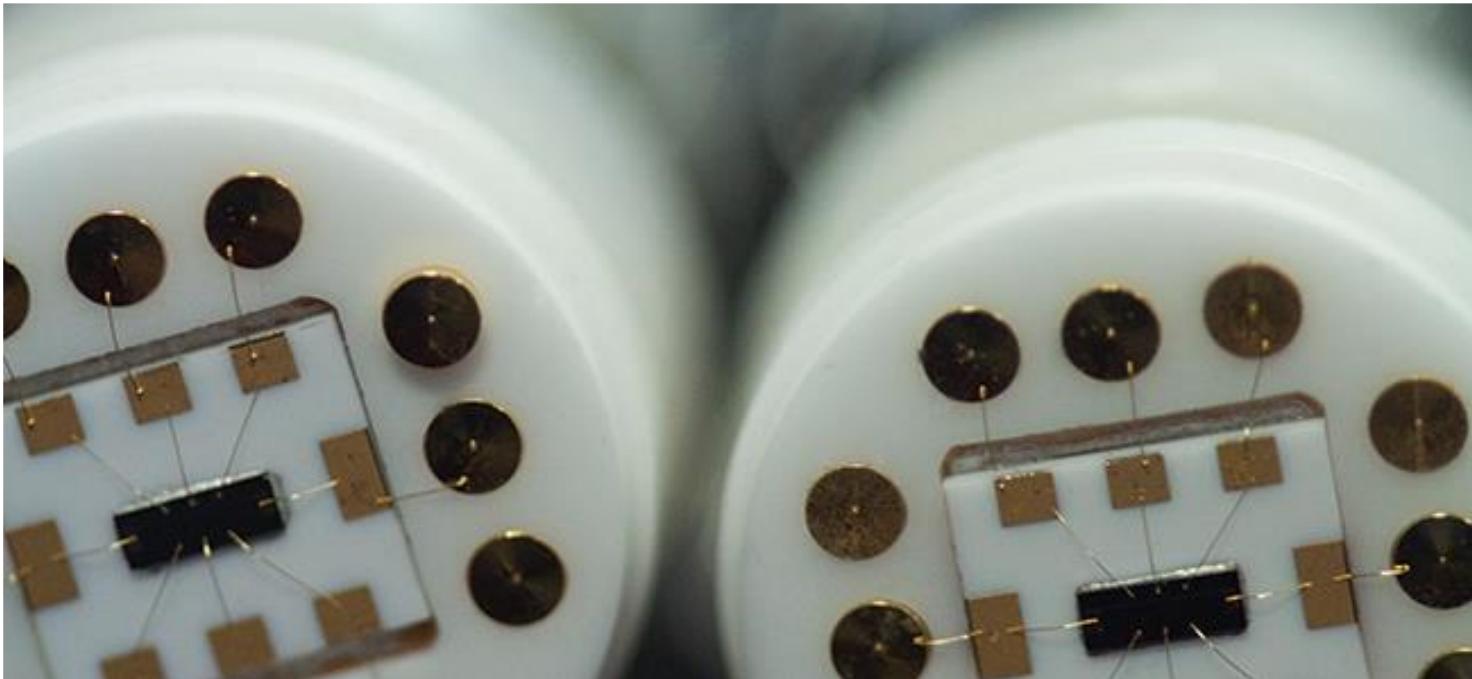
LIBRO Fondamenti della Misurazione
